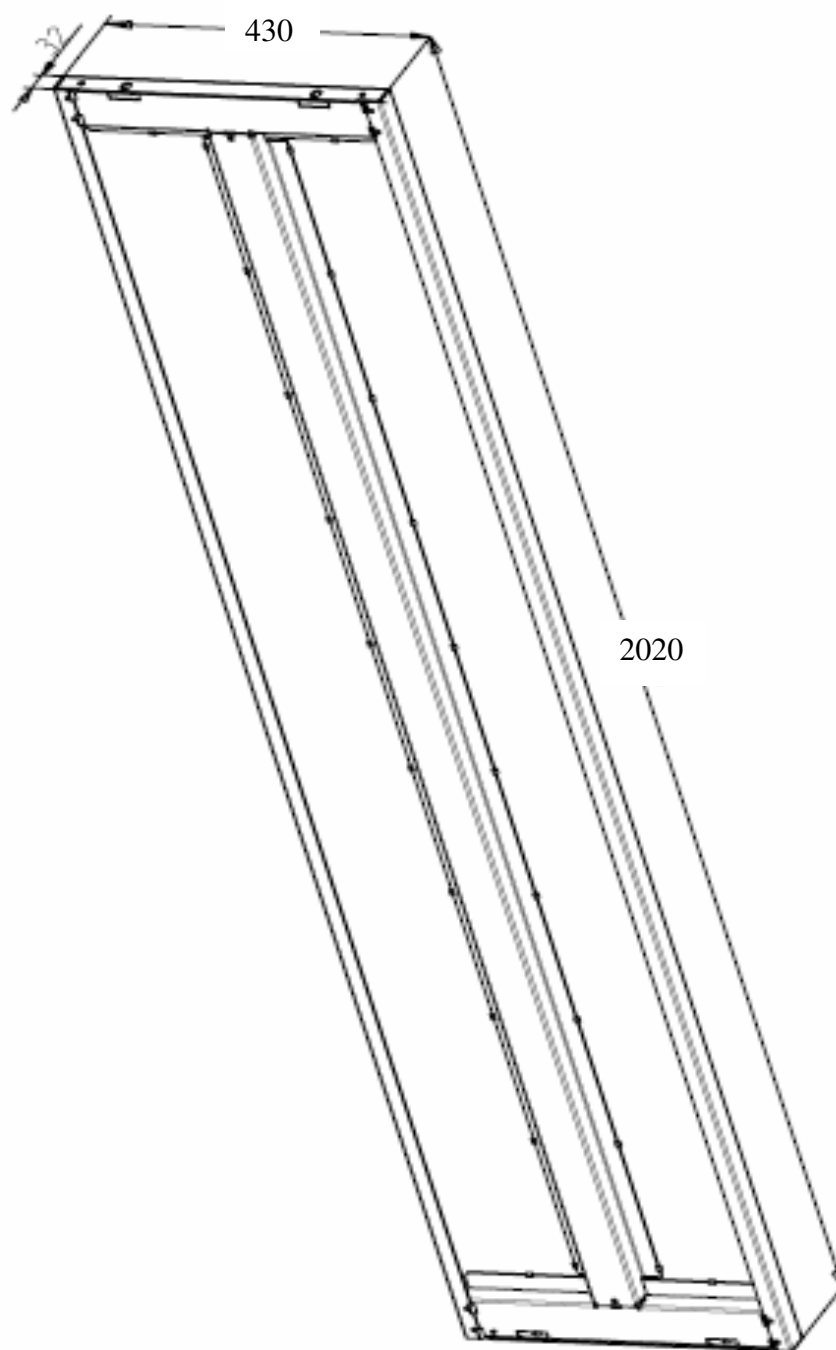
Esquema do Conjunto painel soldado (dimensões em mm)
